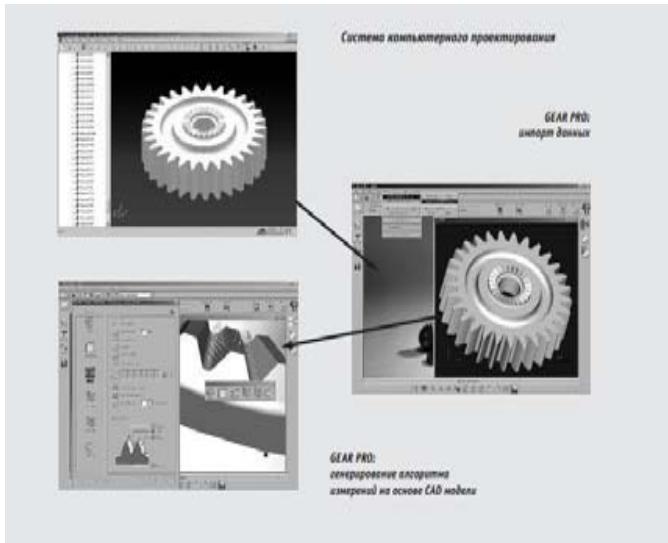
Построение CAD модели измеряемого зубчатого колеса
